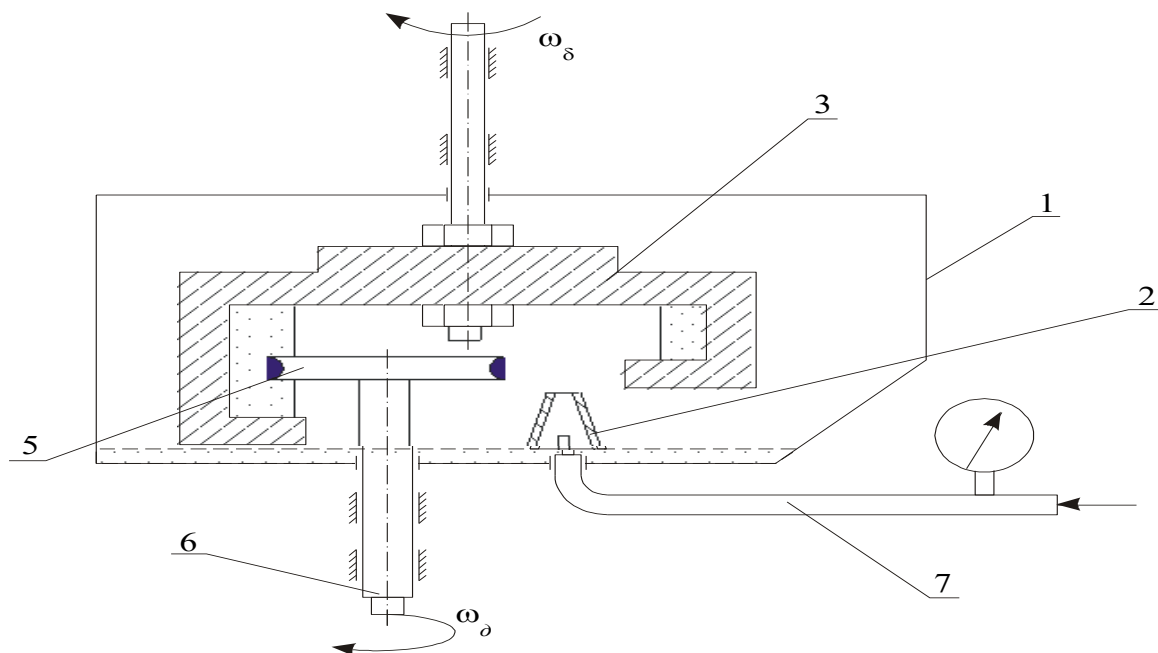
Схема устройства для обработки уплотненным потоком абразивных частиц
